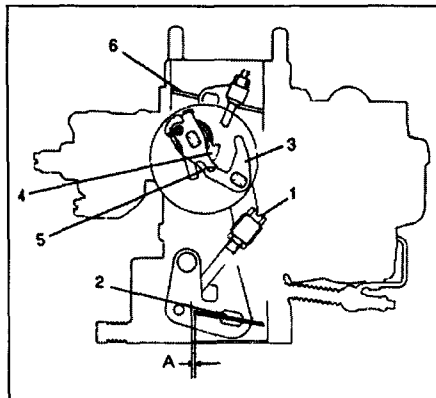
Регулировка пусковых оборотов - полуавтоматический привод
